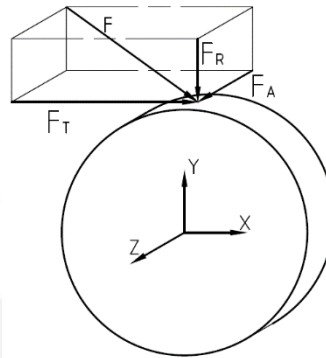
Fuerzas que actúan sobre engranajes de dientes helicoidales
